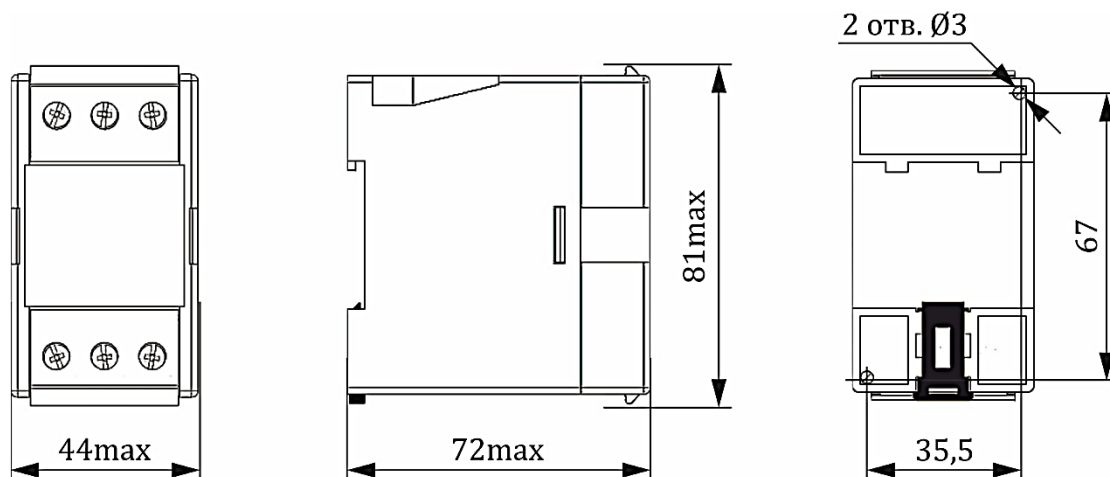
Габаритные и установочные размеры корпуса М6
